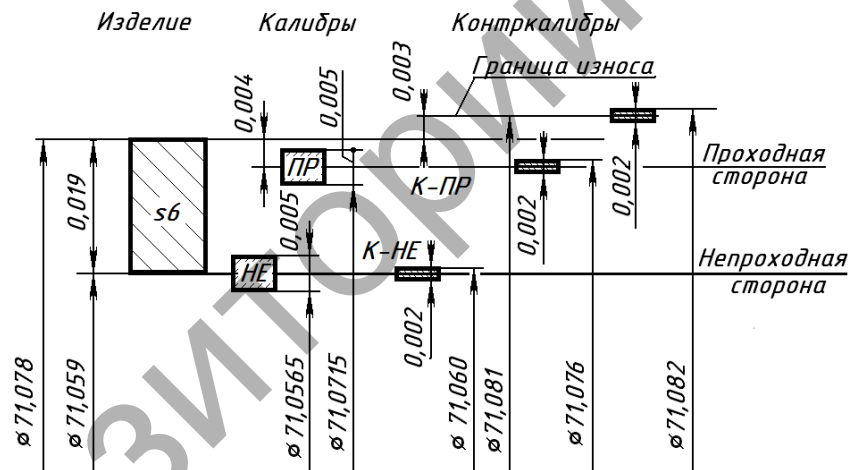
Схема расположения полей допусков рабочих калибров-скоб для вала $\varnothing 71s6$ и контрольных калибров для этих скоб
